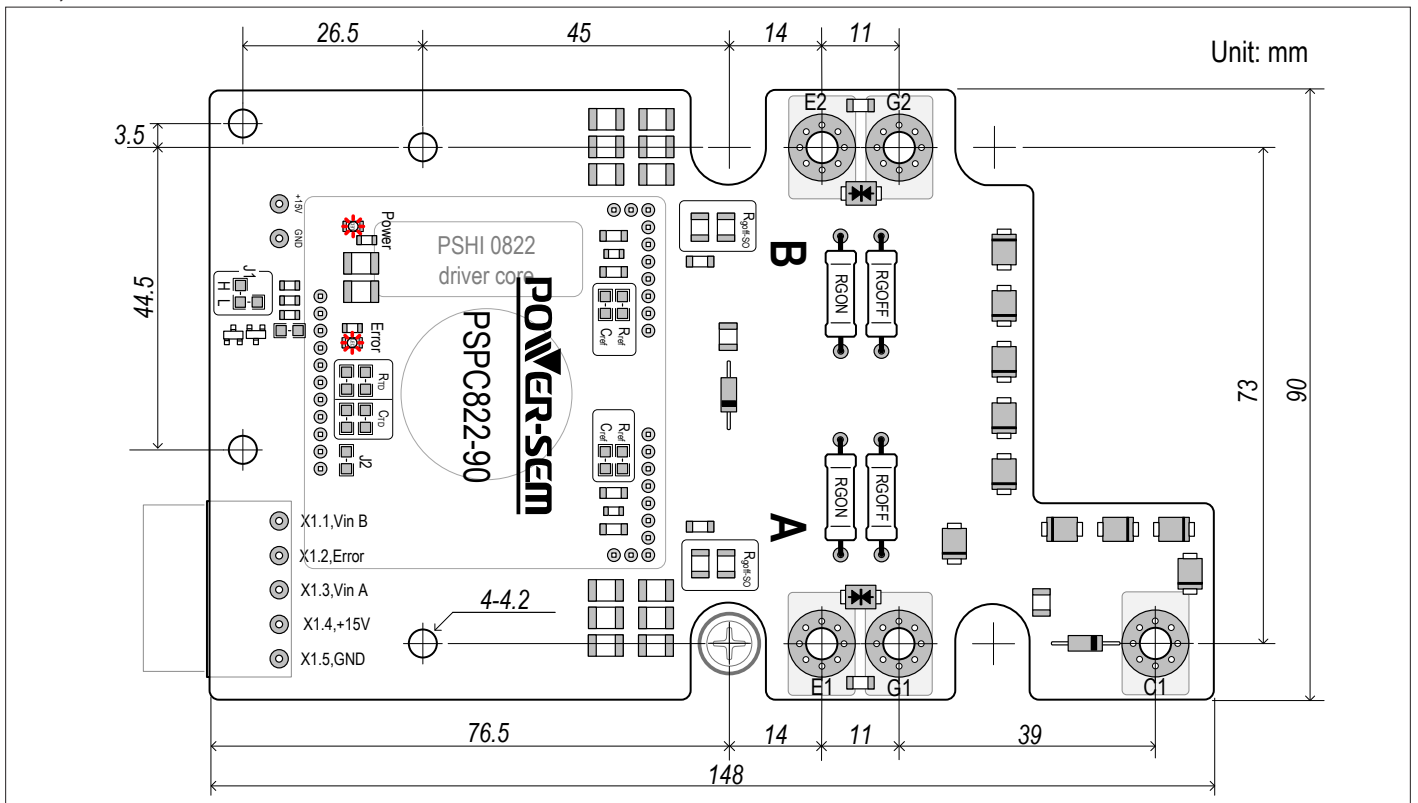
, PSPC 822-90 外形及安装尺寸示意图
